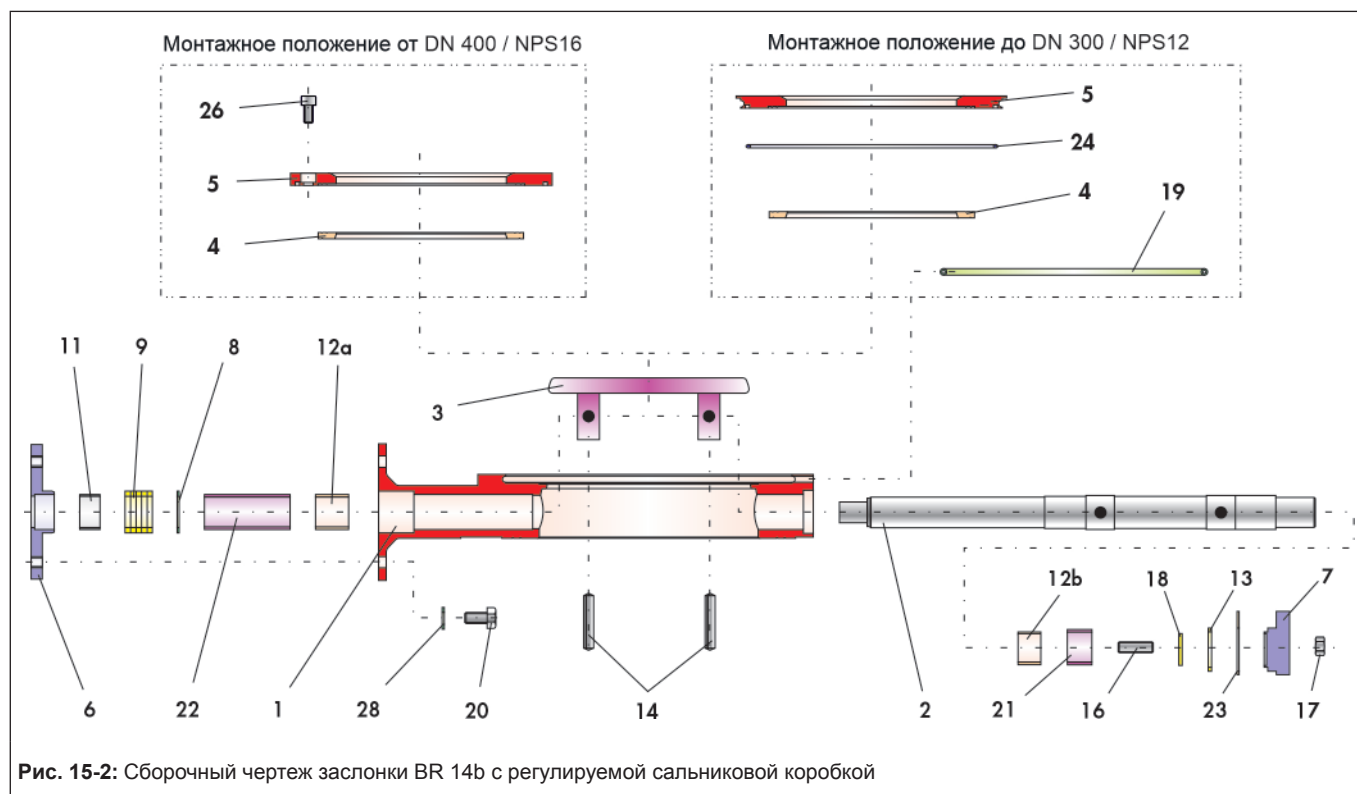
Сборочный чертеж заслонки BR 14b с регулируемой сальниковой коробкой
